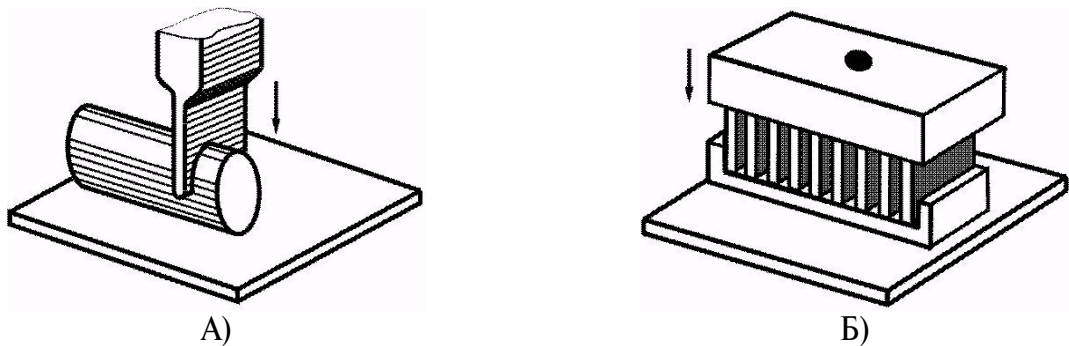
Схема ультразвукового разрезания заготовок:
